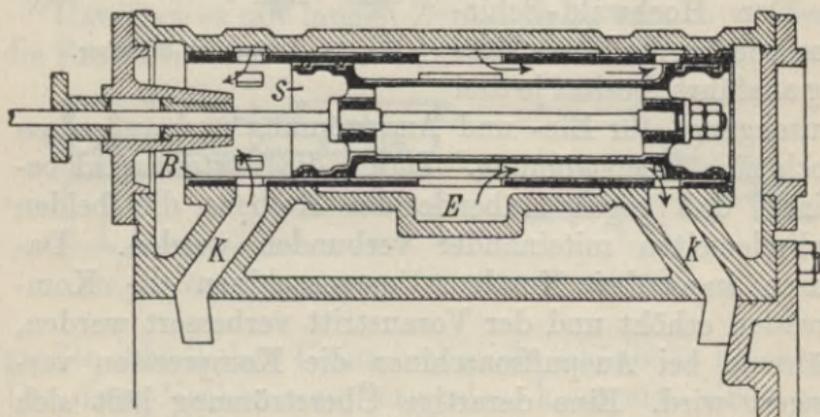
Kolbenschieber mit federnden Dichtungsringen und innerer Einströmung.
